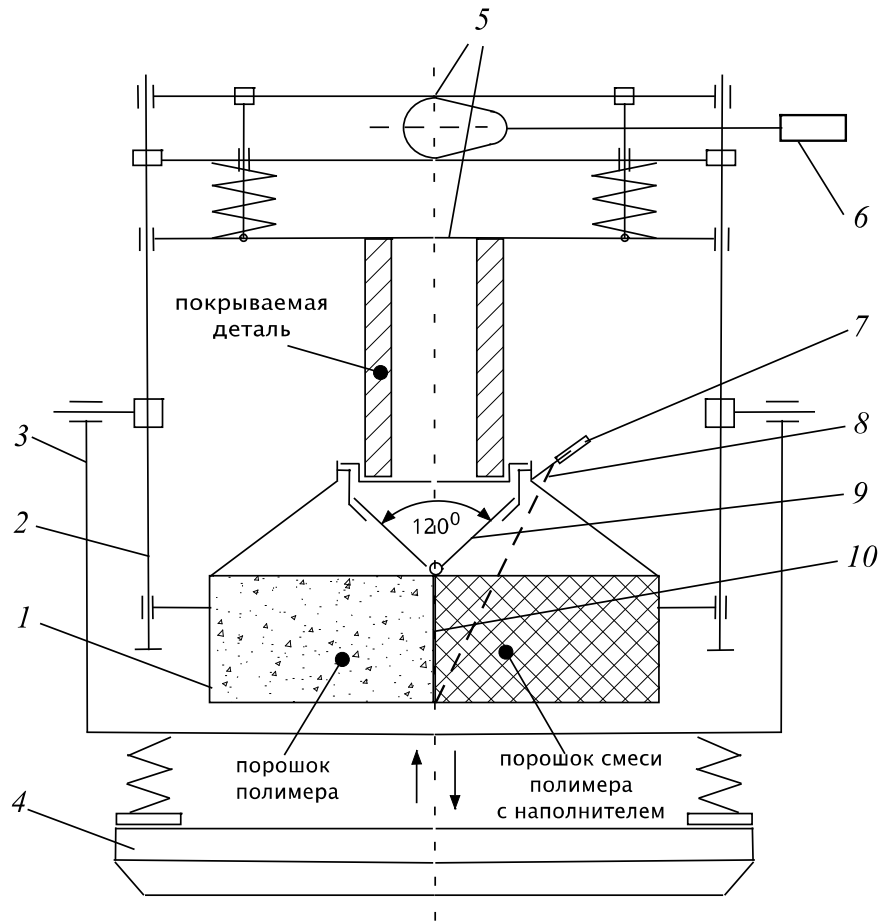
Схема установки для нанесения двухслойных полимерных покрытий
